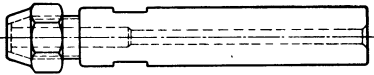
Halter mit Spannmutter für Tieflochbohrer.
